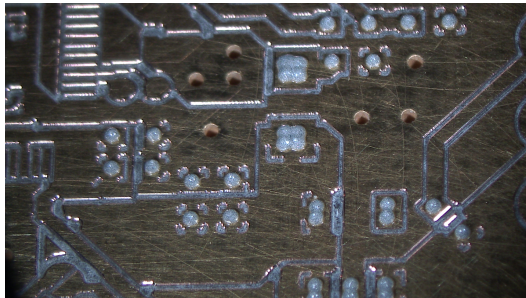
Dispensación pasta de soldadura sobre los pads.
